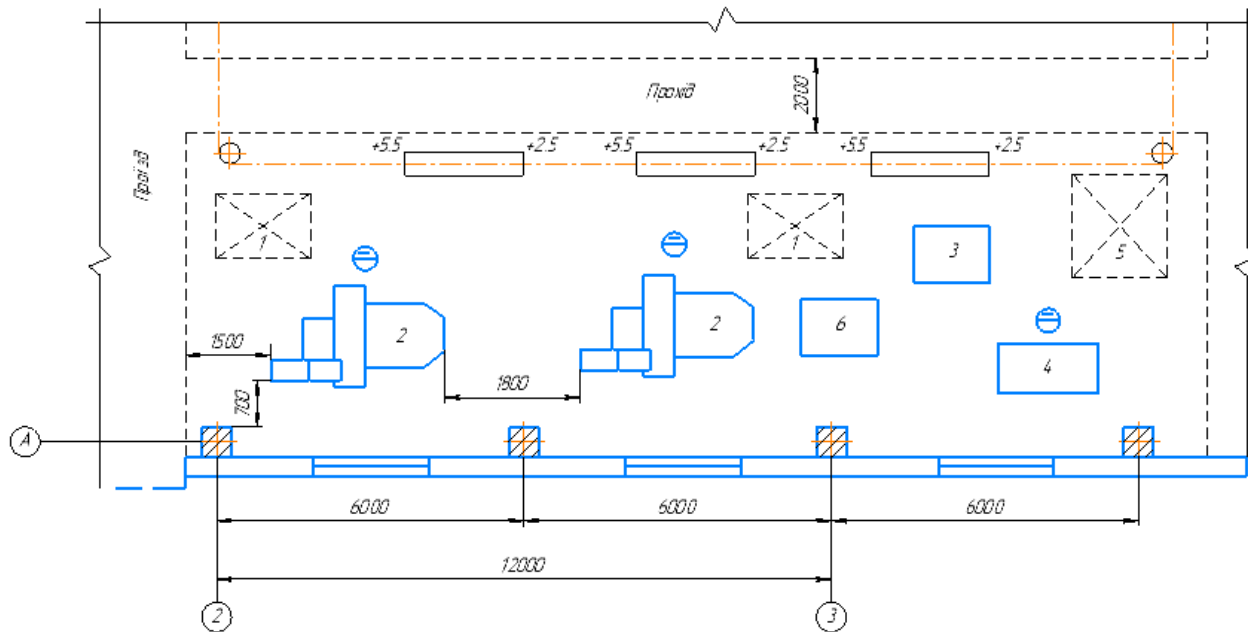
План розміщення устаткування на дільниці механічної обробки корпусу ОЛВ52.122 (1, 5 – місця складування деталей, 2 – оброблюючий центр моделі *IP500ПМФ4*, 6 – слюсарний верстак, 4 – стіл для контролю, 5 – промивна машина)
